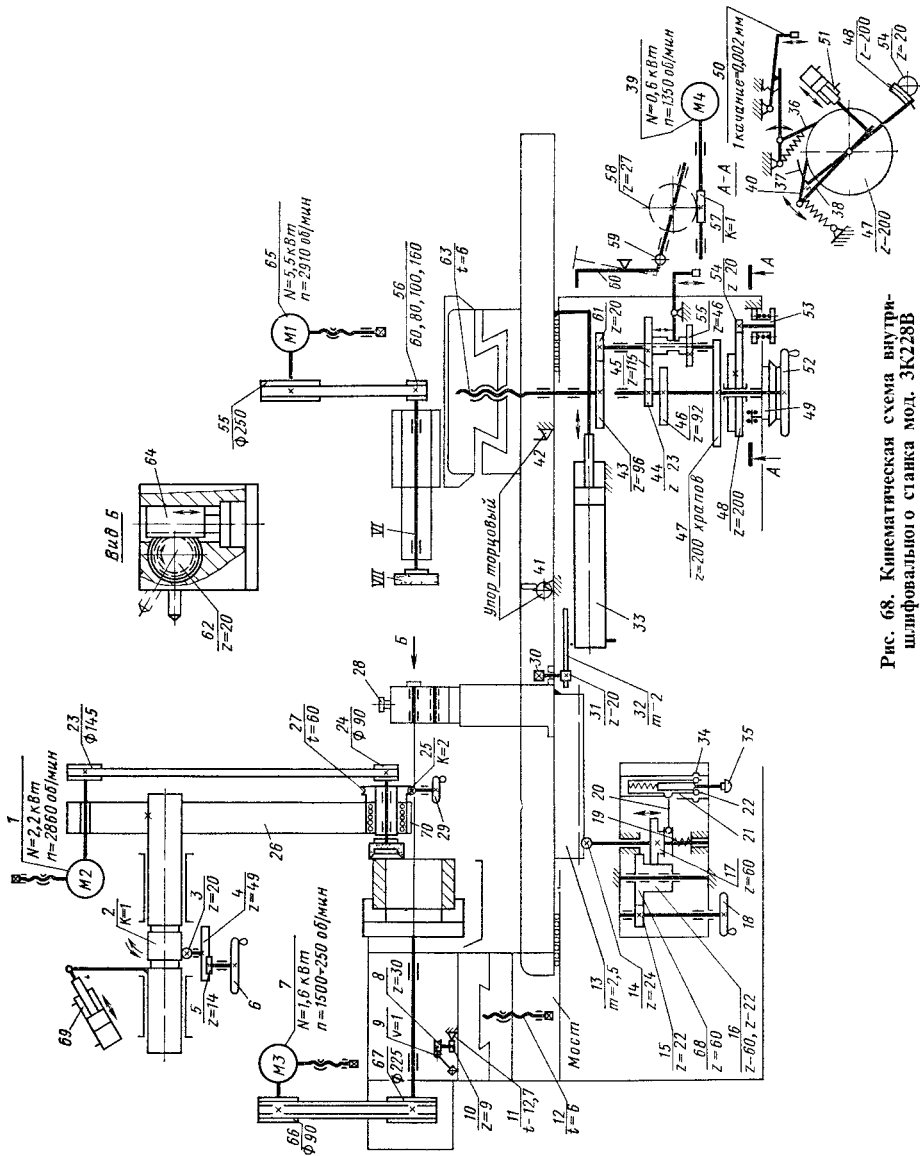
Кинематическая схема внутри-шпильного станка мод. 3К228В
